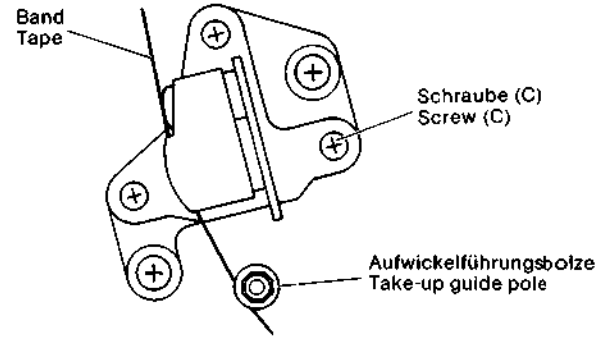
Aufwickel-Führungsbolzen / Take-up guide pole
